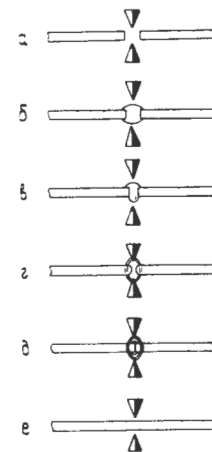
Технологический процесс сварки световодов: а — начальное состояние; б — введение смеси; в — сближение; г — оплавление торцов; д — сближение и сварка; е — окончание сварки.
